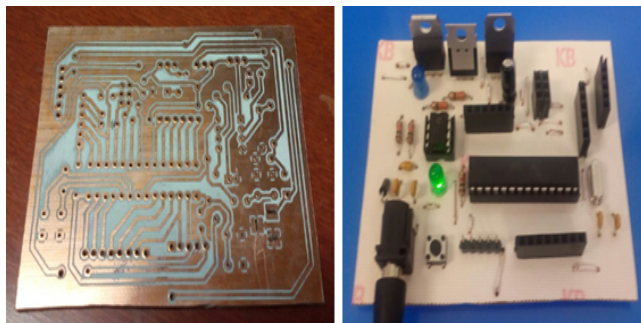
PCB del sistema embebido antes y después de soldar los componentes.
